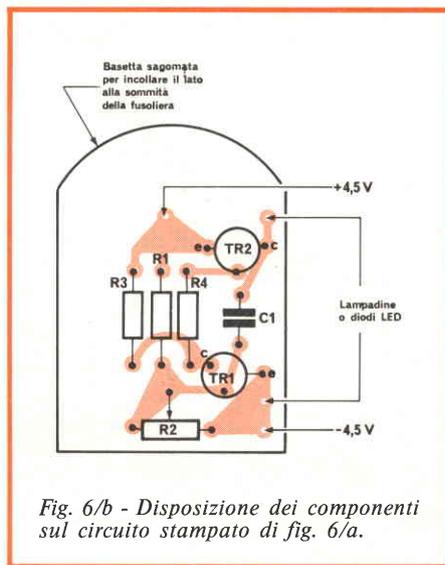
/b - Disposizione dei componenti sul circuito stampato di fig. 6/a.
